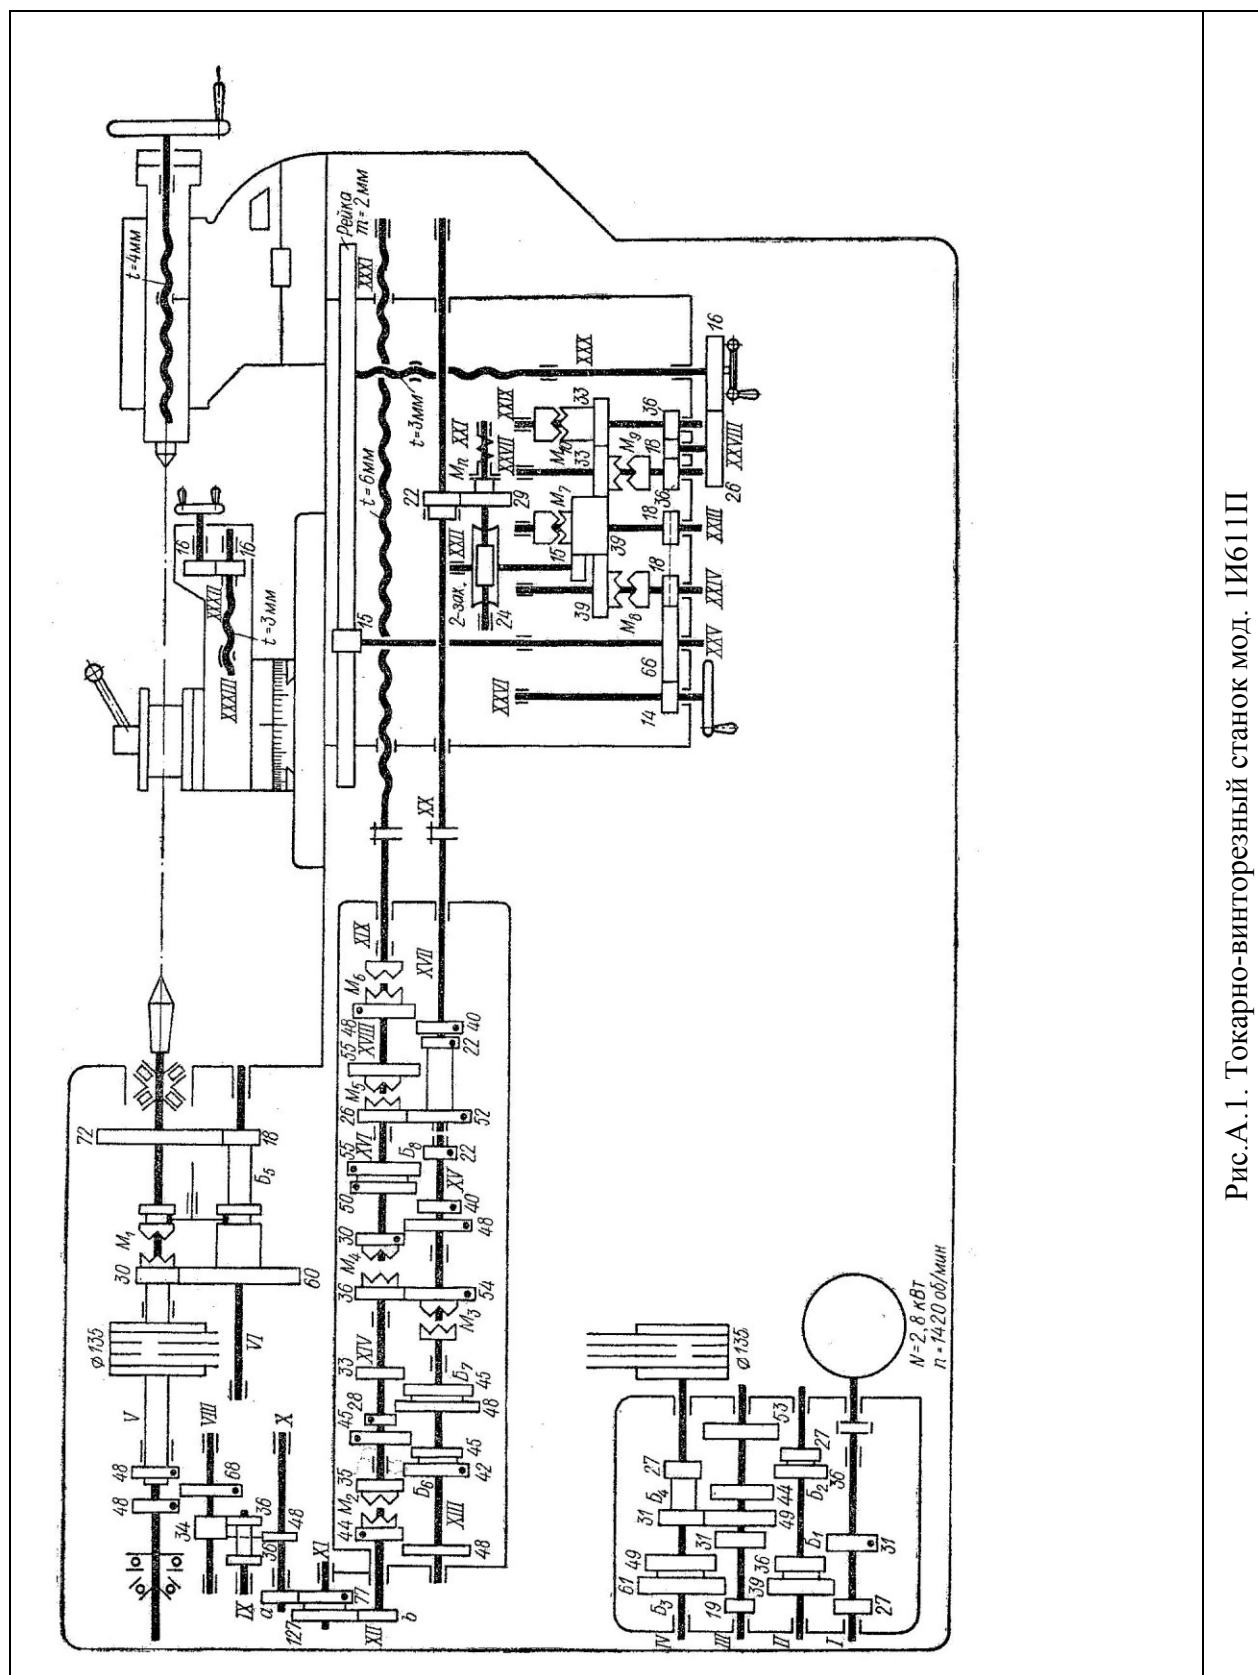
Токарно-винторезный станок мод. 1И611П
